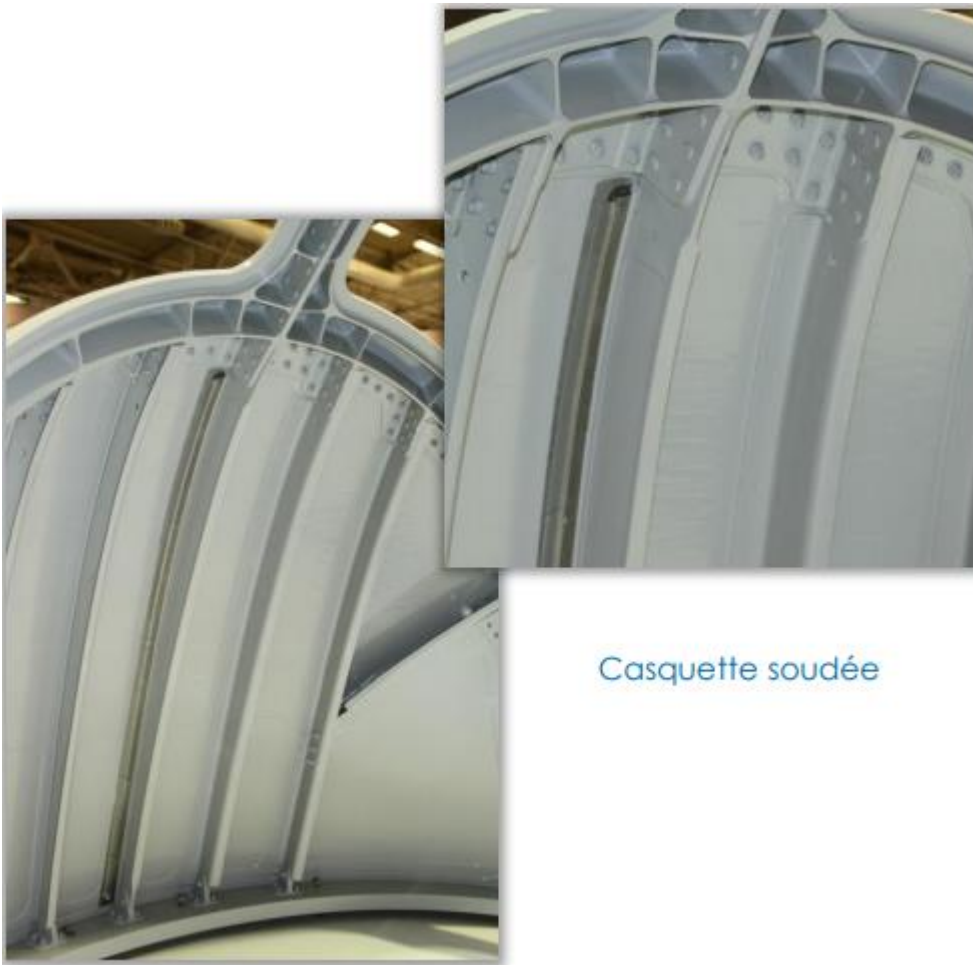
Assemblage d'une casquette d'avion avec le procédé de FSW
